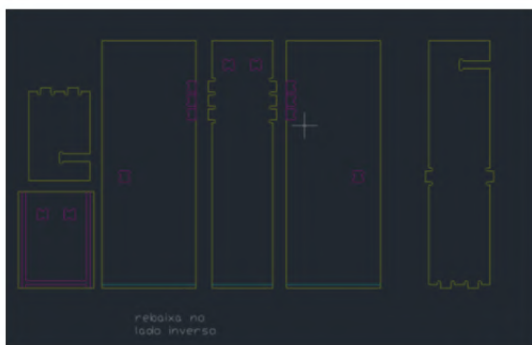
Primeiro ensaio seccional. DXF com layers para fabrico. Elaboração própria (2025).
